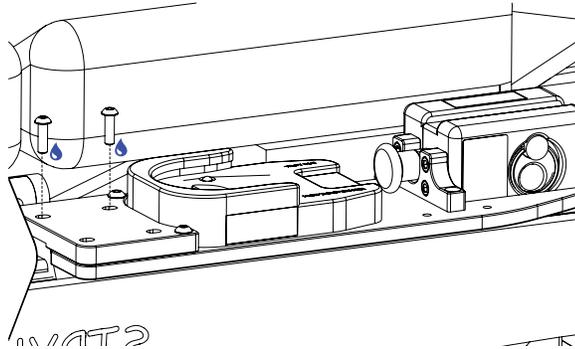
Plaque de support du IV Pro Adapter 2-SMDT installé
